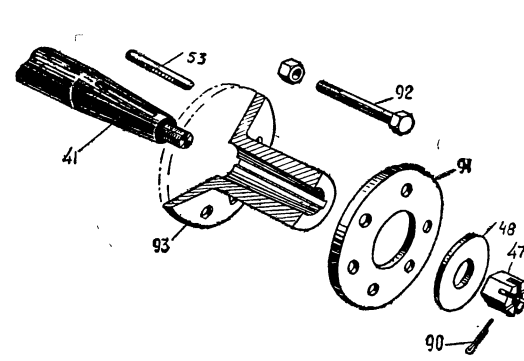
Конец вала воздушного винта с деталями для крепления винта.
